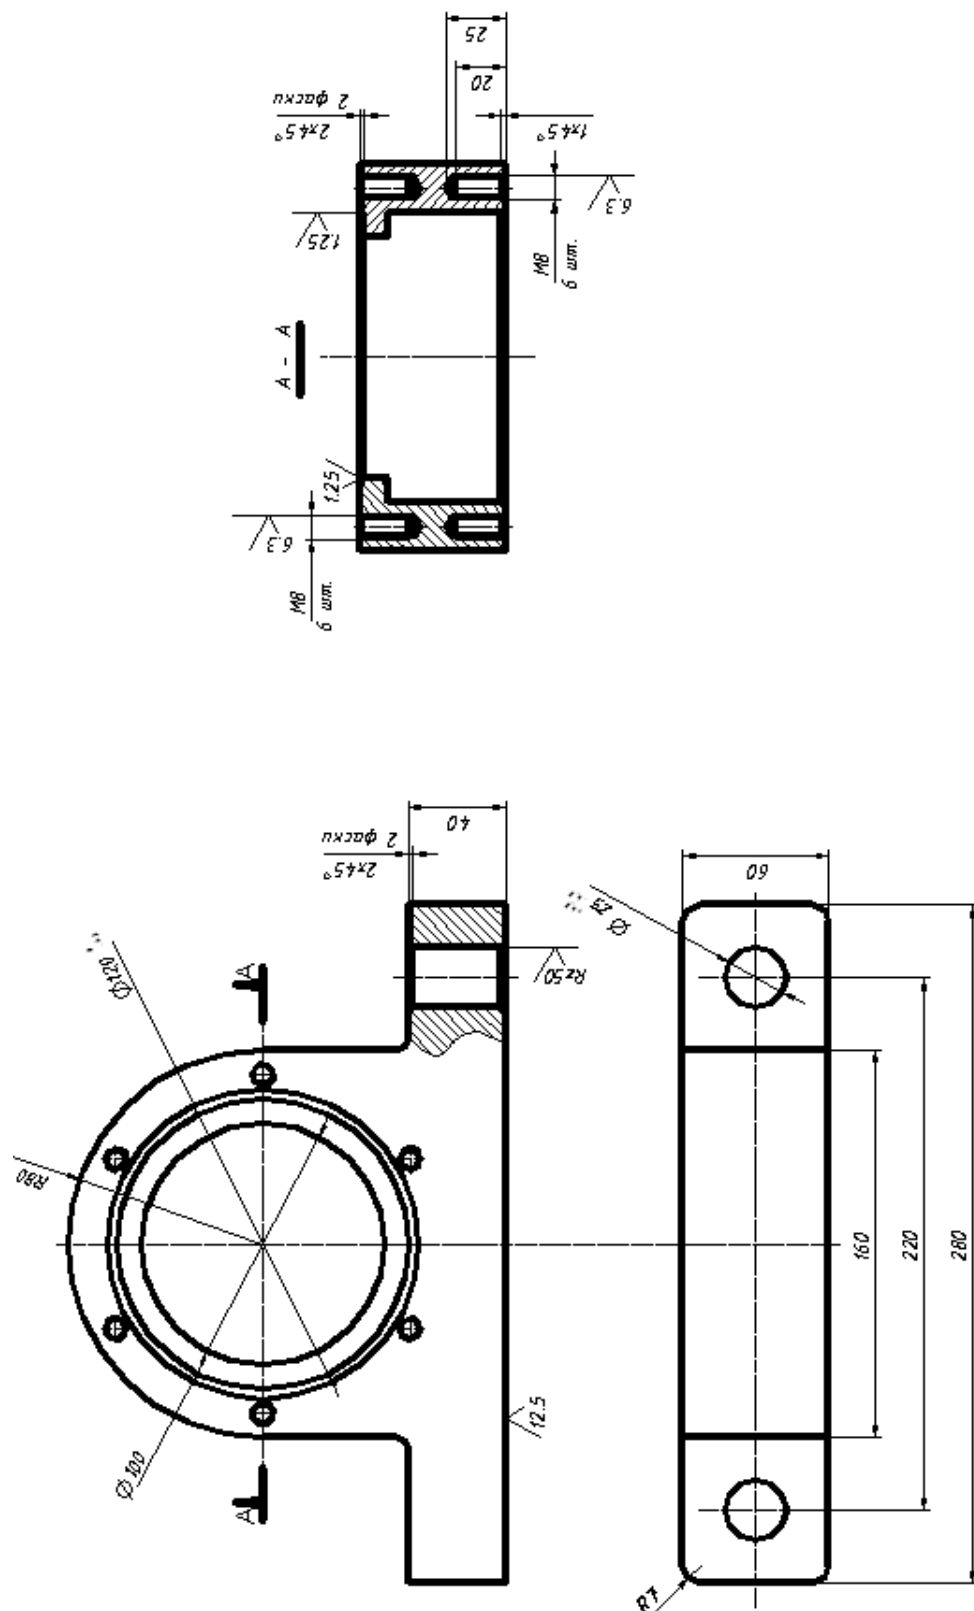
Креслення підшипникової опори (Compas-3D)
